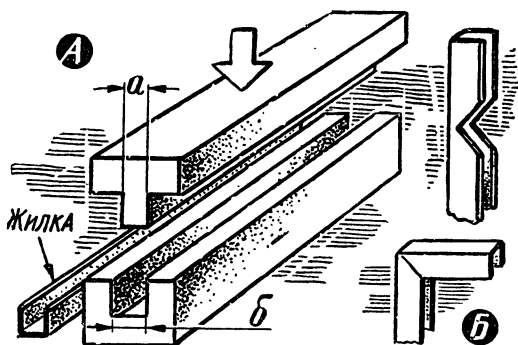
Изготовление витражей: А — штамп для изготовления жилок; Б — изгибание жилки.
